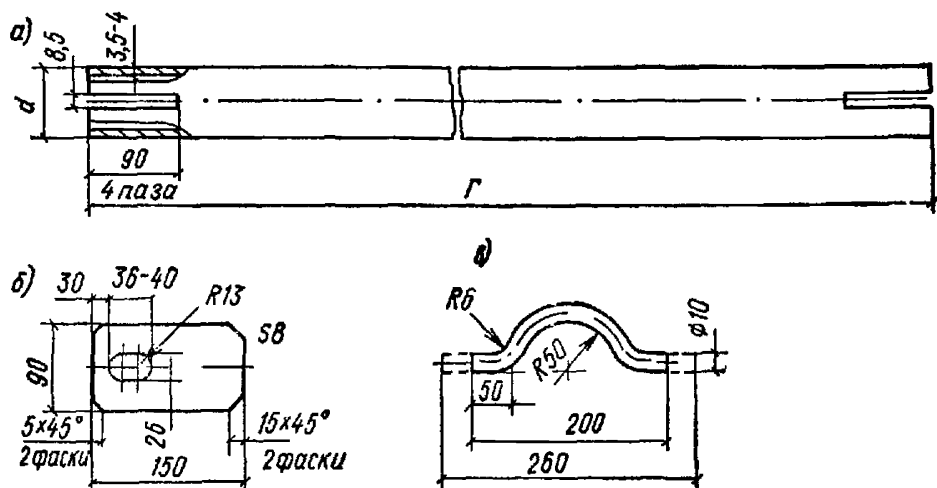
Детали стяжек для рельсовых путей на железобетонных балках
